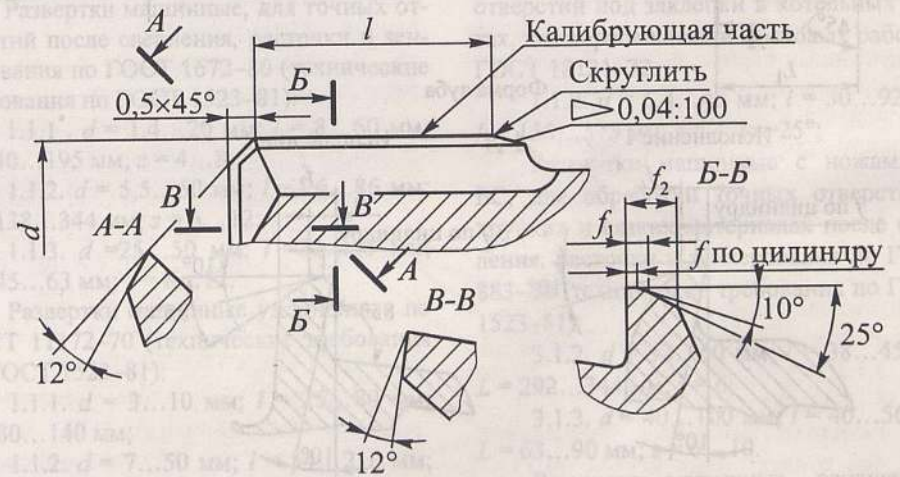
Развертка с торцевой режущей частью и заходной фаской
